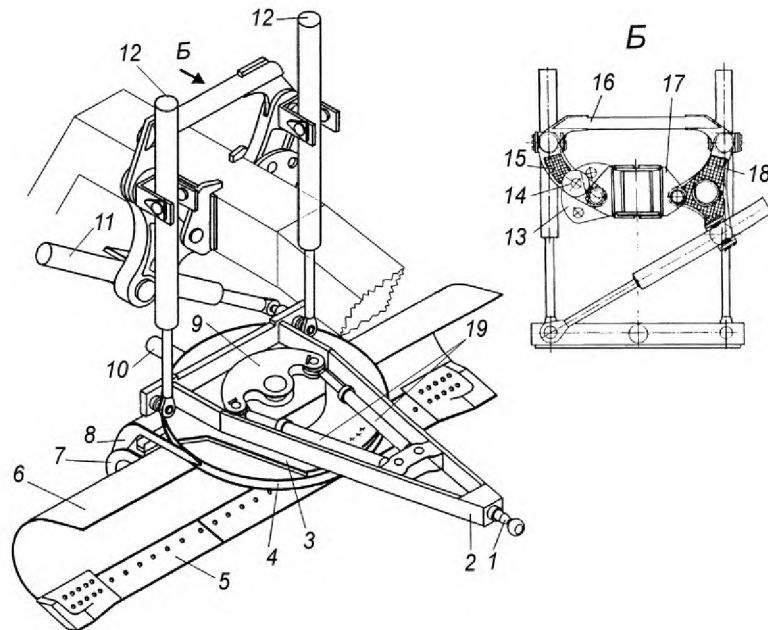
Рабочее оборудование автогрейдера А120: 1 – шкворень; 2 – несущая балка; 3 – опорный лист несущей балки; 4 – поворотный круг; 5 – нож; 6 – отвал; 7 – опора отвала; 8 – кронштейн поворотного круга; 9 – щека поворотного круга; 10 – гидроцилиндр изменения угла резания; 11 – гидроцилиндр выноса тяговой рамы; 12 – гидроцилиндры подъема-опускания отвала; 13, 17 – кронштейны подвески; 14 – поршень-защелка; 15 – левый рычаг; 16 – тяга; 18 – правый рычаг; 19 – гидроцилиндры поворота отвала
